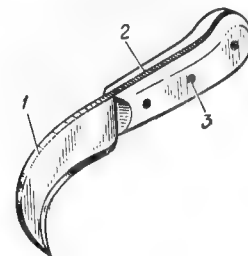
1 — лезвие; 2 — ручка; 3 — заклепка
